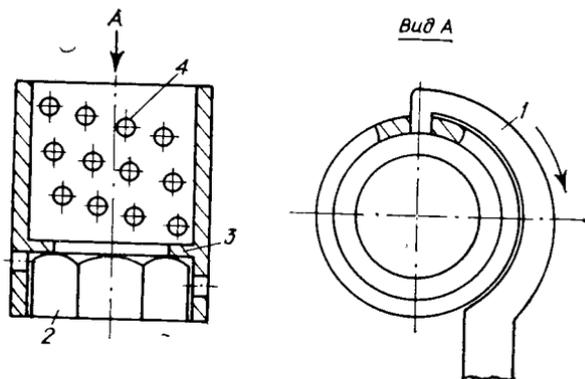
Приспособление для заворачивания резьбовых соединений:
